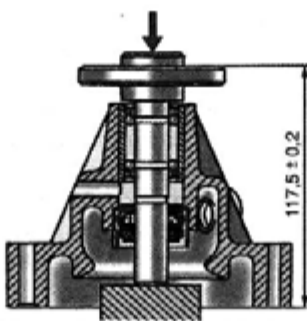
Напрессовка ступицы шкива водяного насоса на вал
